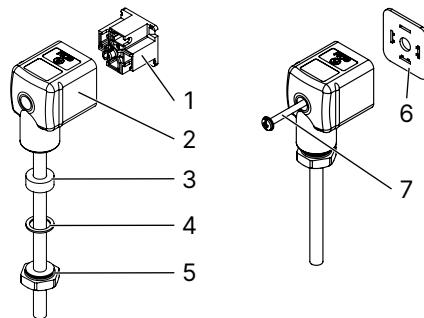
Assemblage du connecteur femelle Type 2518 (fourni)
